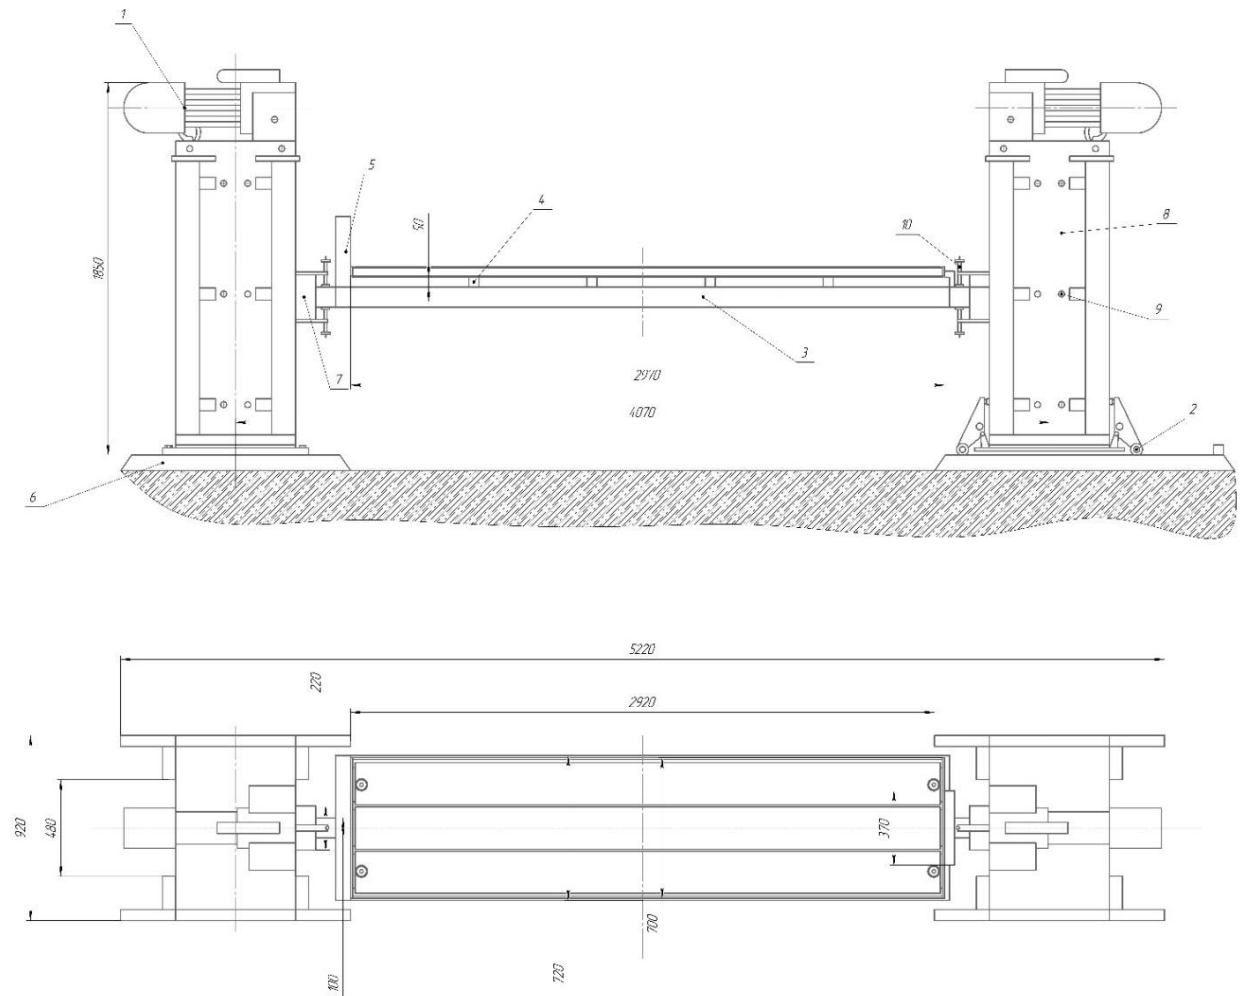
Загальний вигляд кантувача з підйомними центрами КПЦ-4000
